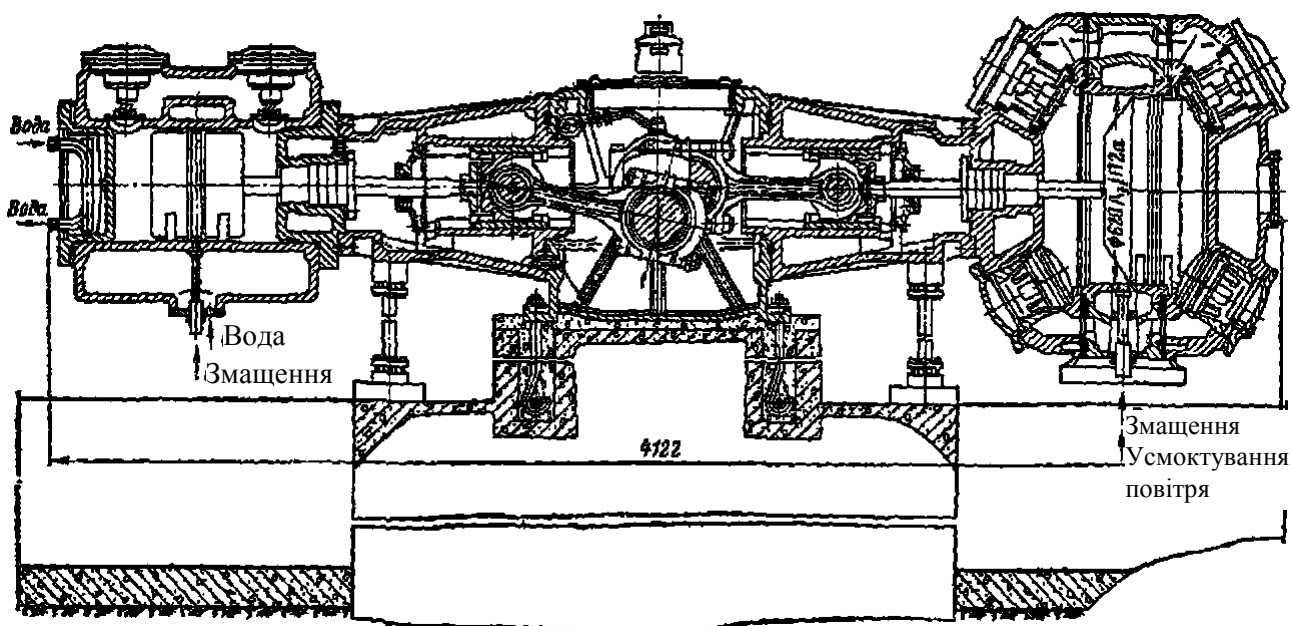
Двоступеневий опозитний компресор для подачі повітря.
